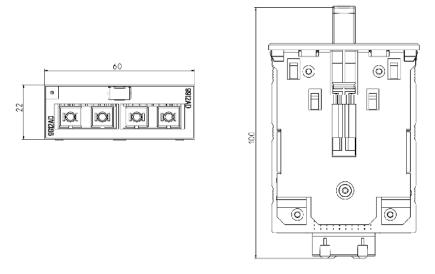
MM900 Dessin coté 4 : Ports optiques SC
